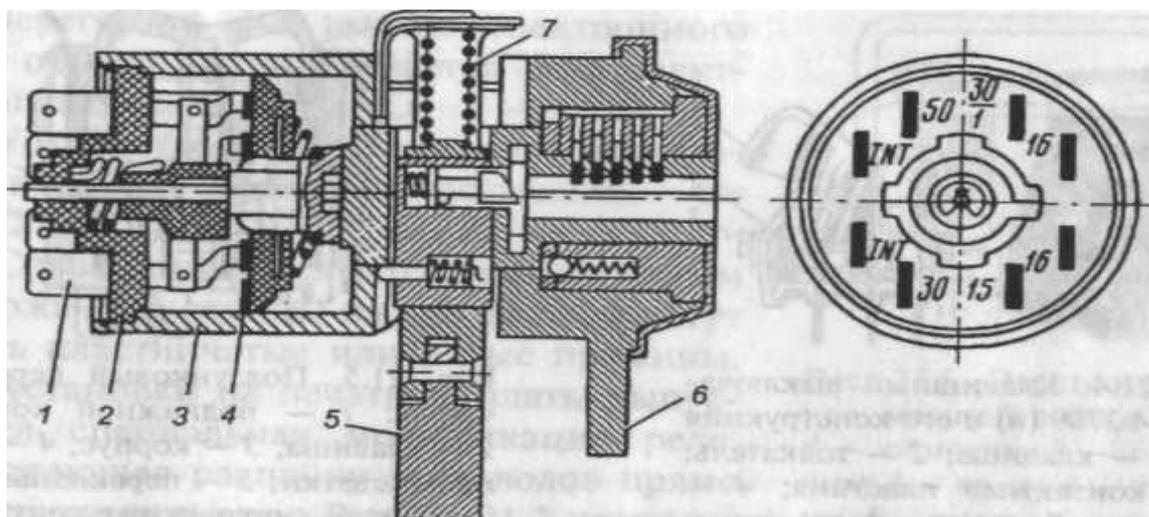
Замок-выключатель ВК347: 1 — вывод; 2 — панель; 3 — корпус; 4 — контакт; 5 — запорный стержень; 6 — выступ; 7 — пружина
